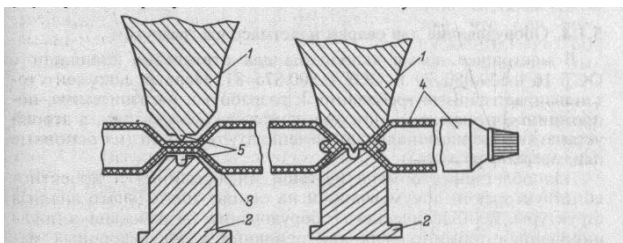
Схема ультразвуковой сварки с одновременной резкой изделий из пластмасс: 1 - волновод-нож; 2 - опора с пазом; 3,4 - части разрезаемой детали; 5 - режущая грань ножа-волновода
